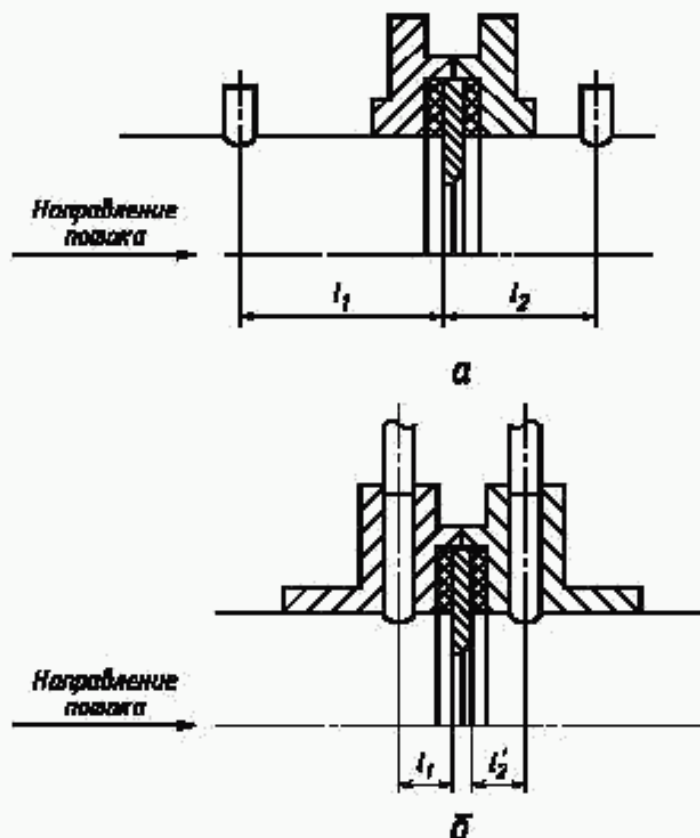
Расположение отверстий для трехрадиусного и фланцевого способов отбора давления
